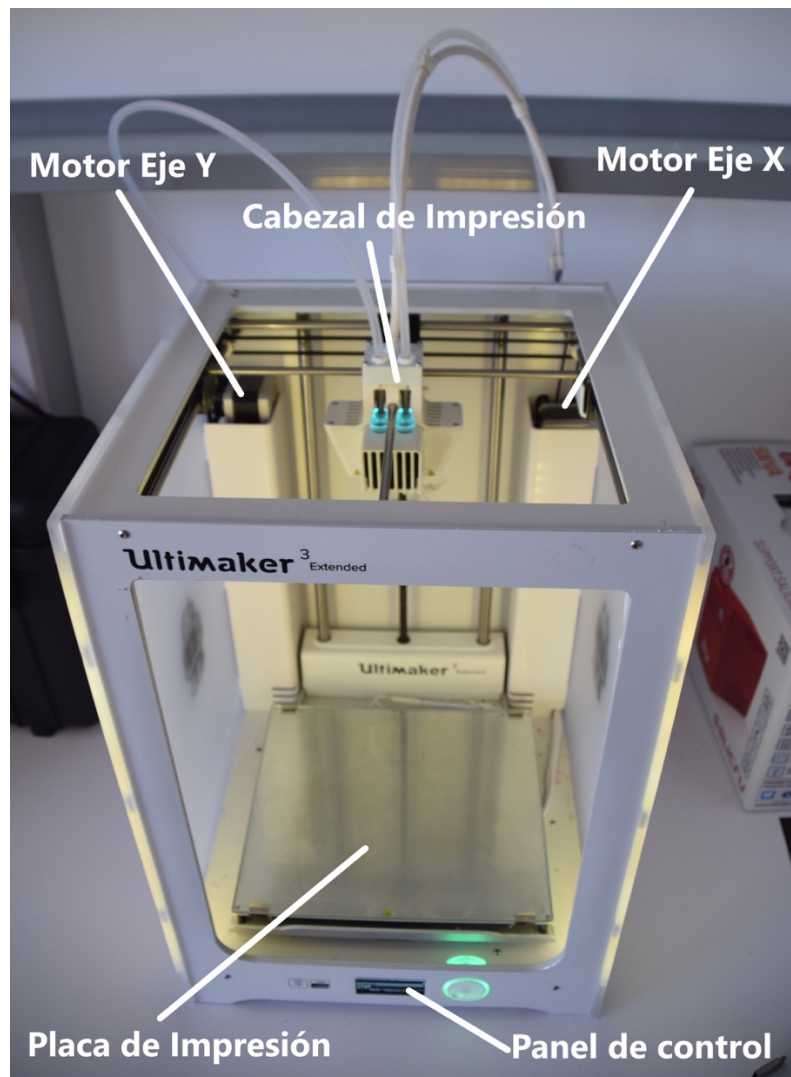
Parte frontal Ultimaker 3 (Elaboración propia)
